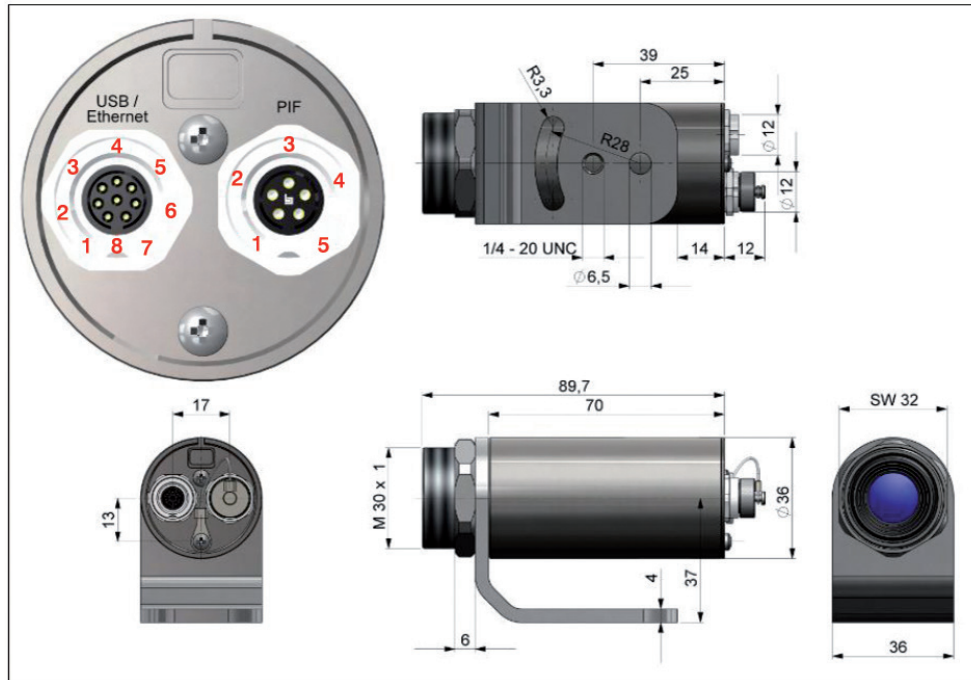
Maßzeichnung thermoMETER TIM 8, Abmessungen in mm
